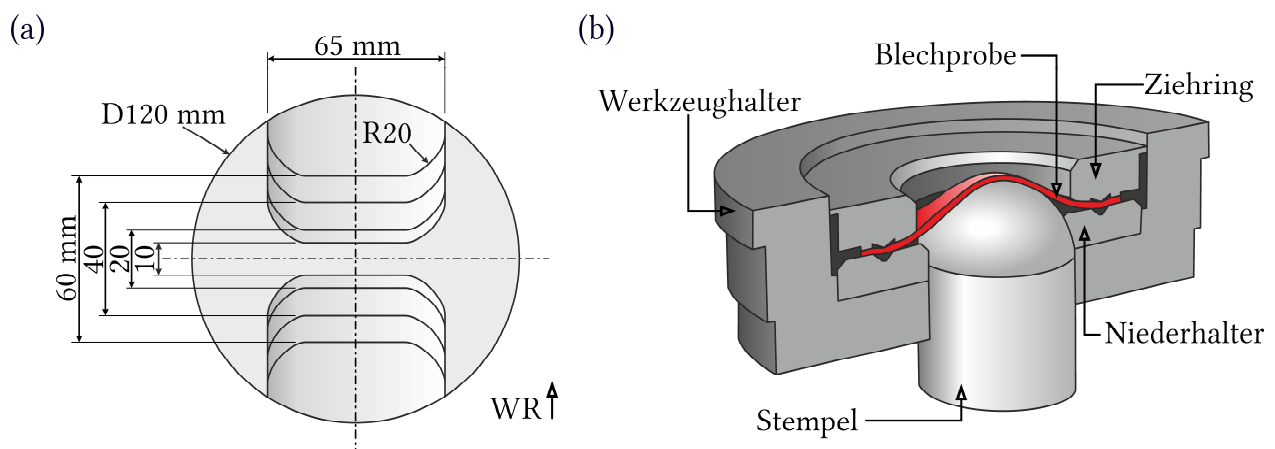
Abmessungen der fünf unterschiedlich taillierten Blechproben (a); Schnittansicht des Streckziehwerkzeugs mit umgeformter Blechprobe (b)
